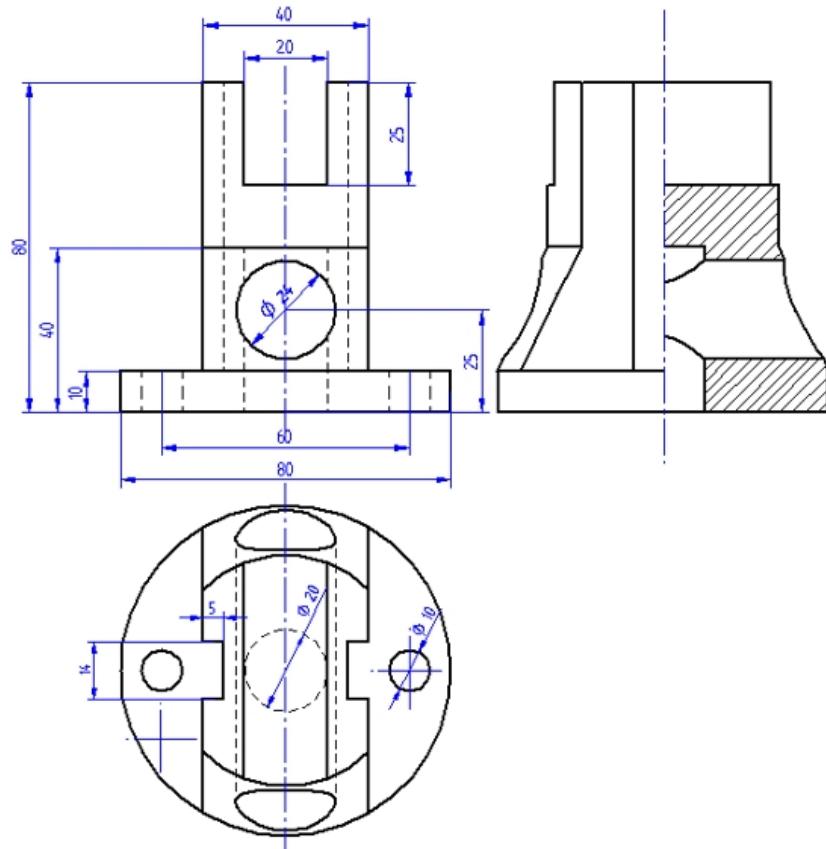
Werkzeichnung mit drei Ansichten, Seitenansicht im Halbschnitt
